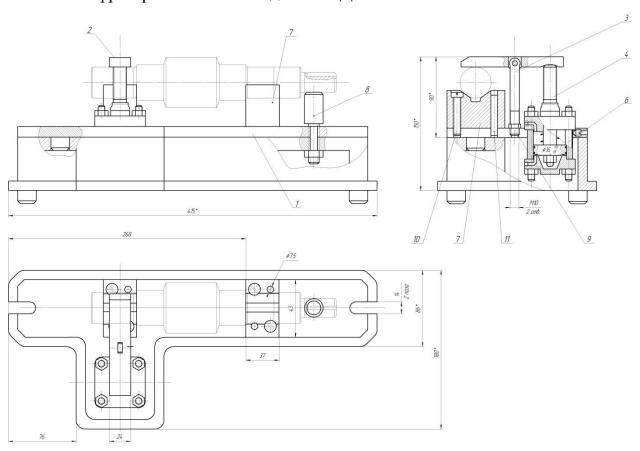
Приспособление для шпоночно-фрезерной операции
